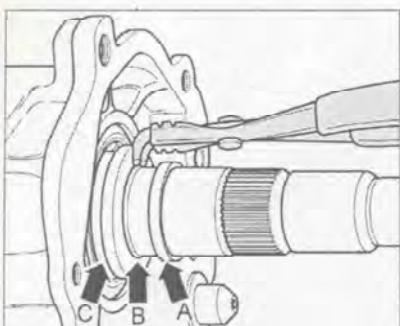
Снимите с вала фрикционное кольцо (стрелка А) игольчатого подшипника шестерни 6-й передачи. С помощью щипцов снимите стопорное кольцо (стрелка В) роликоподшипника. Снимите внутреннюю обойму (стрелка С) роликоподшипника.
